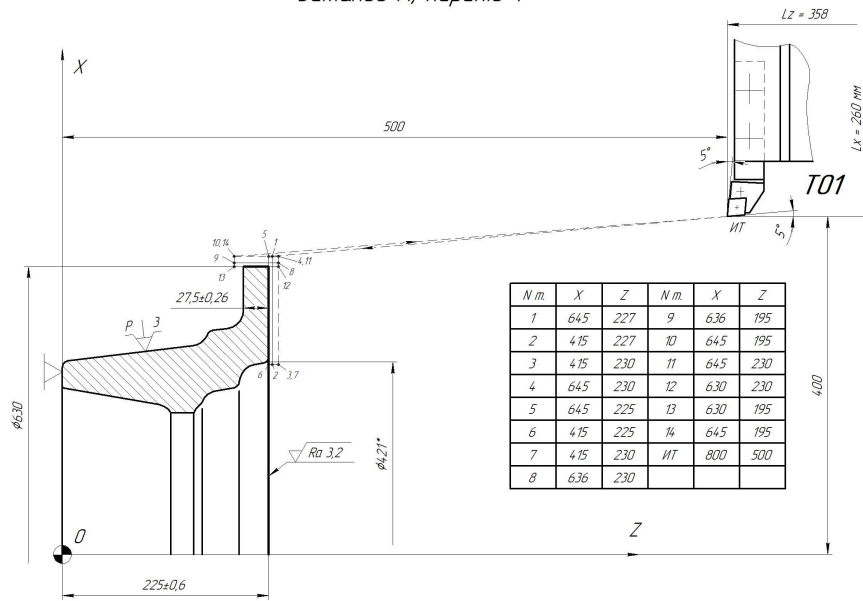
Установ А, перехід 1: схема обробки деталі та координатне розташування інструмента
